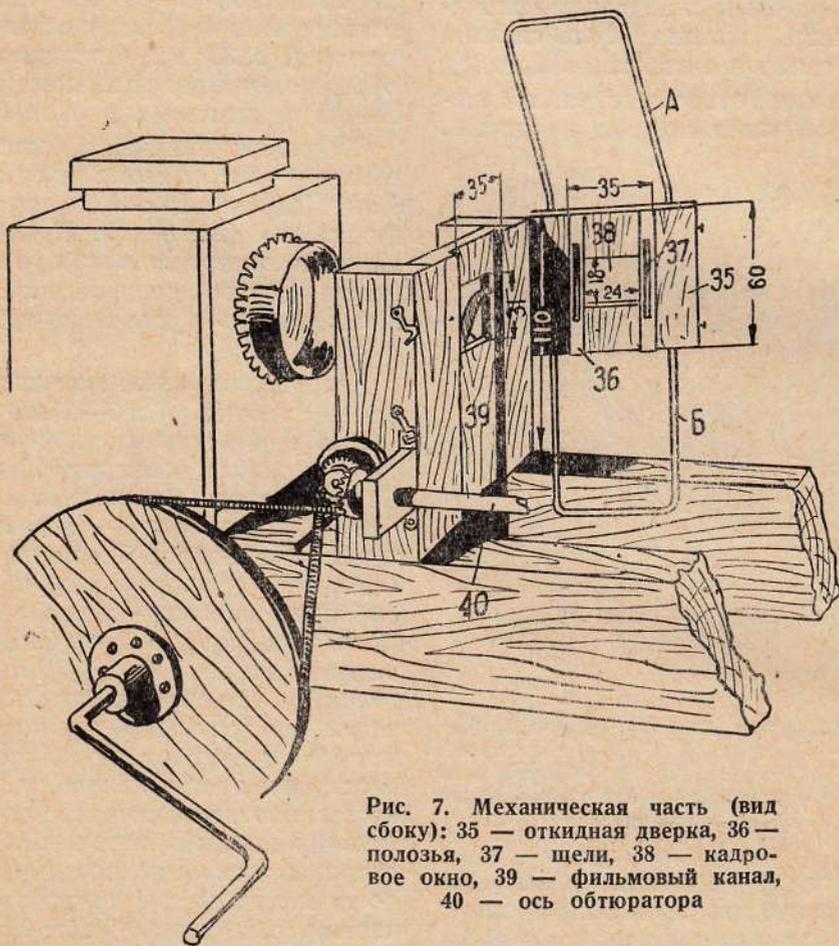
Механическая часть (вид сбоку): 35 — откидная дверка, 36 — полозья, 37 — щели, 38 — кадровое окно, 39 — фильмовый канал, 40 — ось обтюратора
